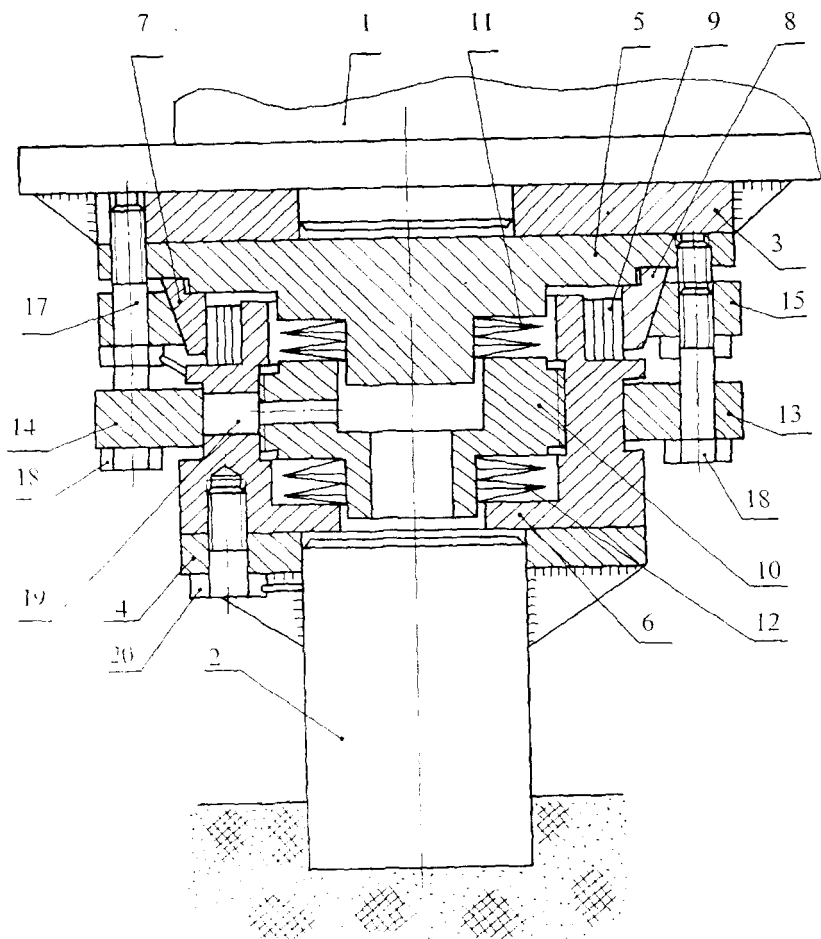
9. Упругодемпферная подвеска основания мельницы для размла какао-бобов РС-1000: 1 - корпус мельницы; 2 - основание; 11, 12 - наборы кольцевых гофрированных шайб (или тарельчатых пружин); 5, 10 - промежуточные направляющие; 9 - радиальный пакет кольцевых гофрированных дисков; 7, 8 - набор конических секторов; 3, 4 - промежуточные основания; 15 - зажимная конусная обойма; 13, 14 - технологические полукольца; 17, 18, 20 - крепежные элементы; 19 - технологическое отверстие (паз).
